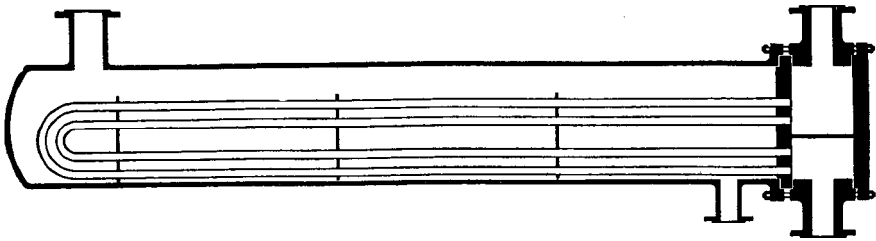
Enfriador (*Patterson Foundry and Machine, Co.*)
